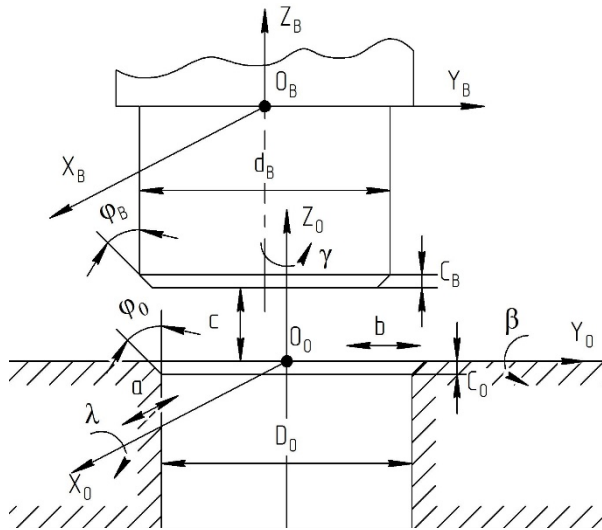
Установка ниппеля в отверстие корпуса
